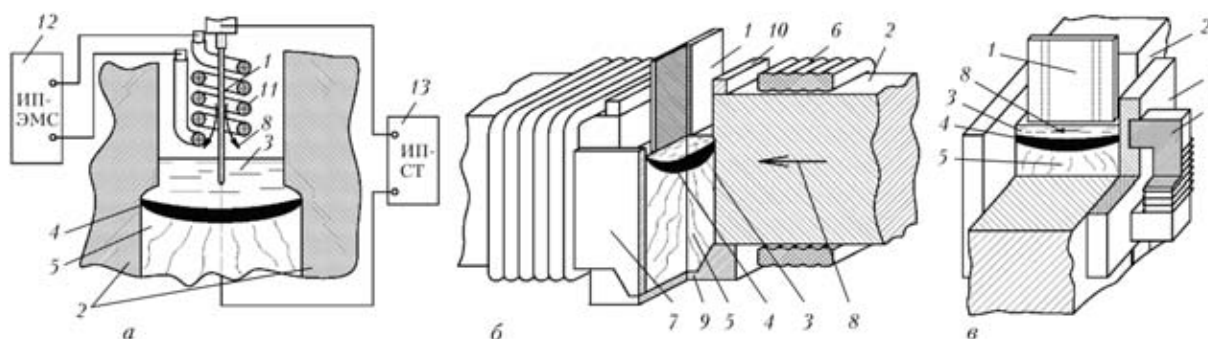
Схема ЭШС в продольном (а) и поперечном (б, в) магнитных полях: 1 — плавящийся мундштук-электрод; 2 — свариваемые изделия; 3 — шлаковая ванна; 4 — металлическая ванна; 5 — сварной шов; 6 — электромагнитное устройство; 7 — формирующие планки; 8 — линии магнитного поля; 9 — входной карман; 10 — выводные планки; 11 — соленоид; 12 — источник питания электромагнитной системы; 13 — источник питания сварочного тока
